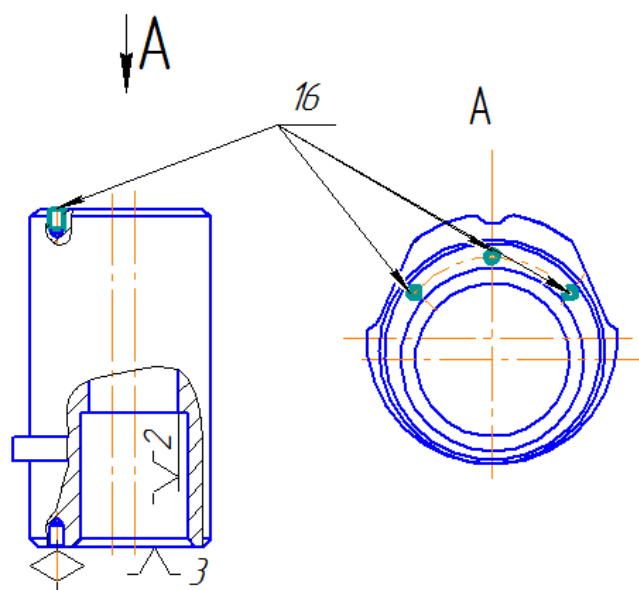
Эскиз фрезерной операции с ЧПУ 045 (Установ Б)
